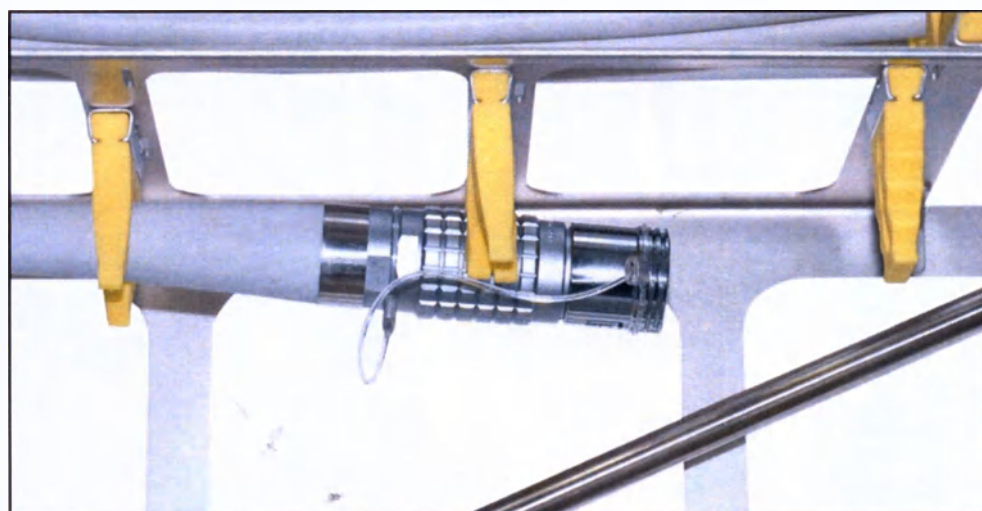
разъем кабеля камеры, закрепленный в нижних держателях
